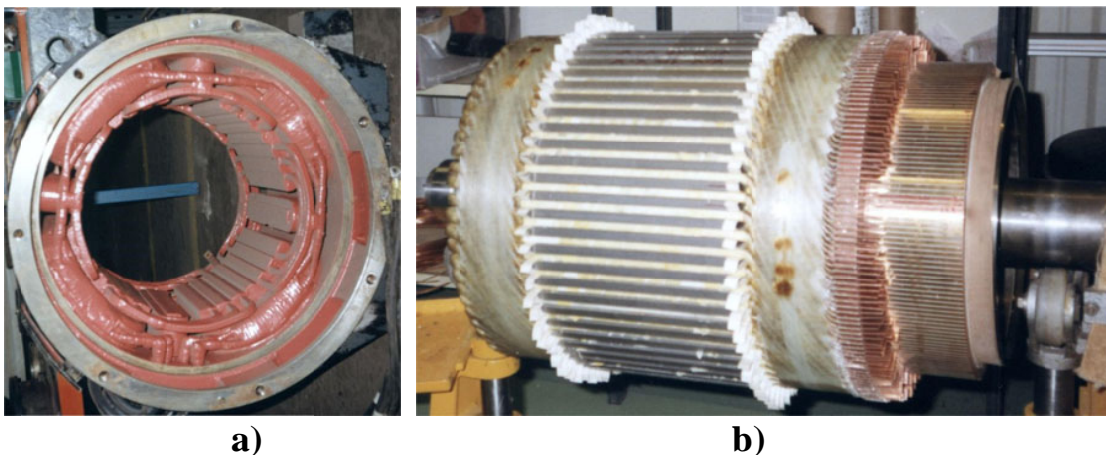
a) Estator y b) rotor de una máquina de c.c. durante su proceso de fabricación.
